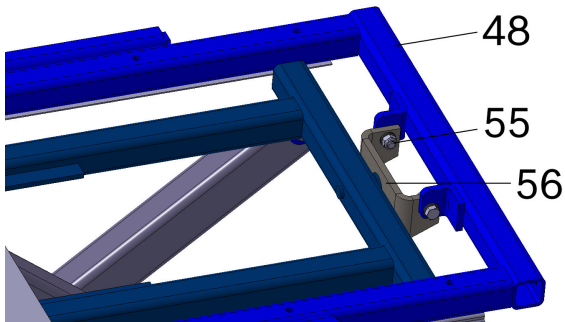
Piano elevatore a pantografo senza piattaforme dall'alto
